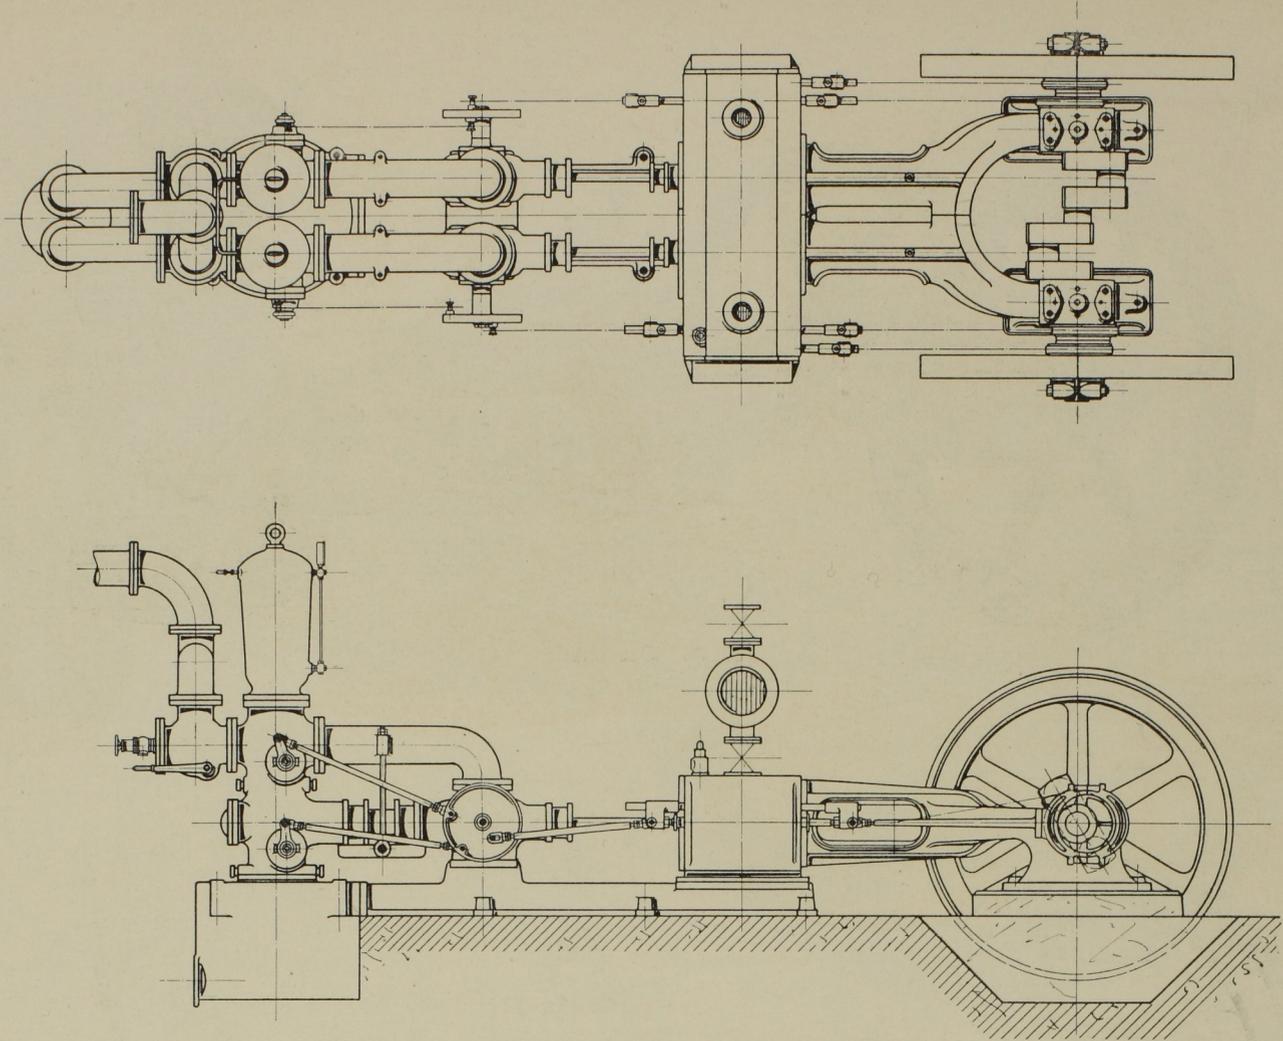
Seitenansicht und Grundriss. Massst. 1 : 32.
